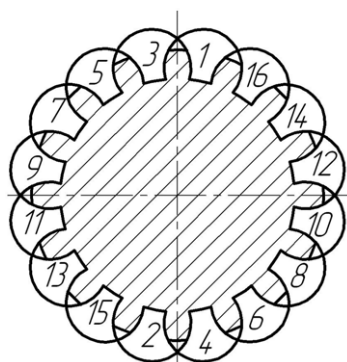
Схема продольной наплавки шлицевой поверхности детали способом уравновешивающих валиков
